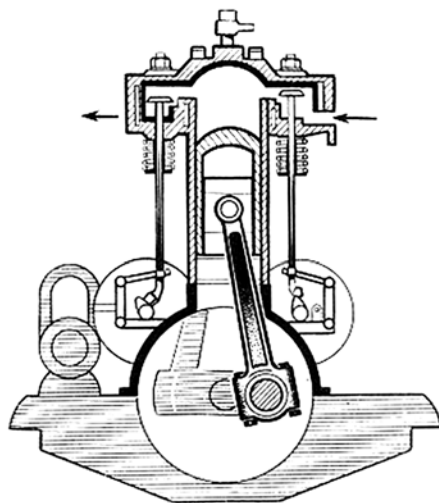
16-сильный двигатель с Т-образной головкой цилиндров конструкции Луцкого
